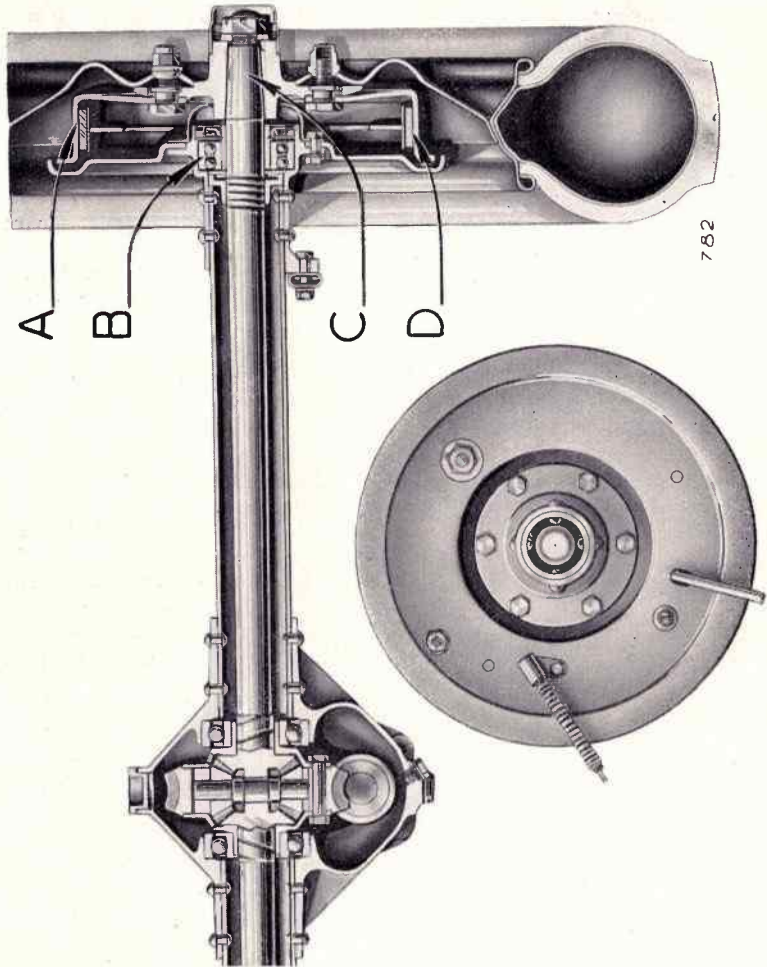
Coupe du pont arrière et vue d'un frein.
